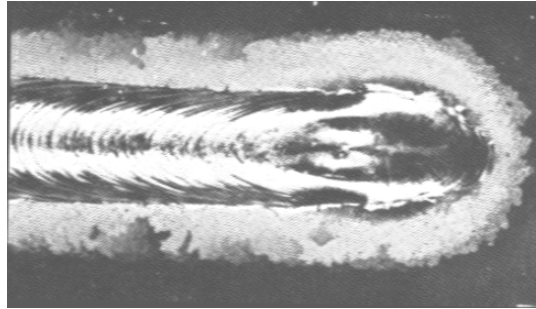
Superfície de uma solda em alumínio mostrando a região de limpeza catódica.
